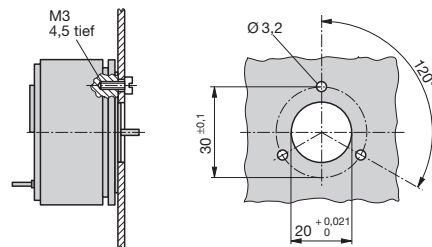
Bohrplan für Befestigung mit 3 Zylinderschrauben M3.
